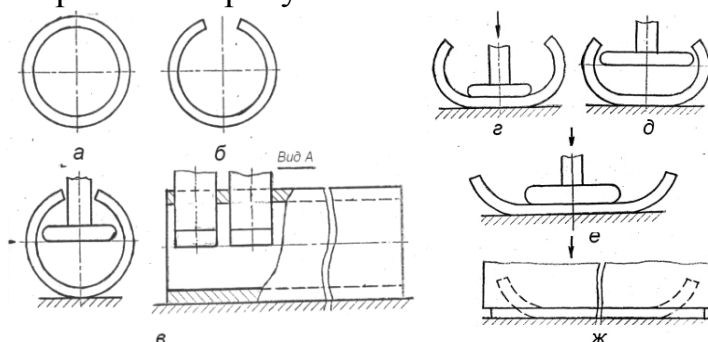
Схема развертки трубной заготовки плоскими бойками [3]
